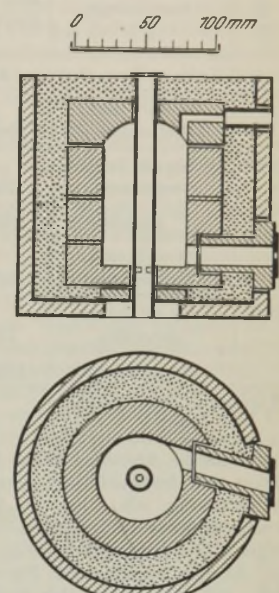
Ausführung des mit Petroleum gefeuerten Gebläseofens.
